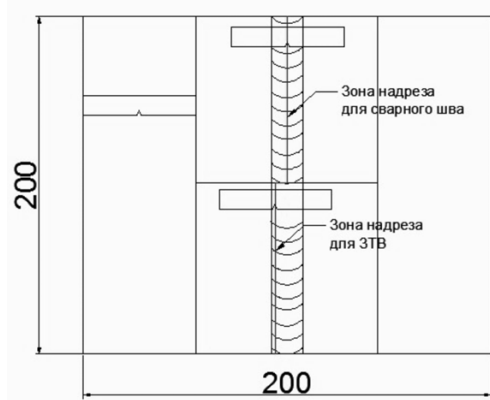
Схема вырезки образцов на ударный изгиб основного металла, МШ и ЗТВ
